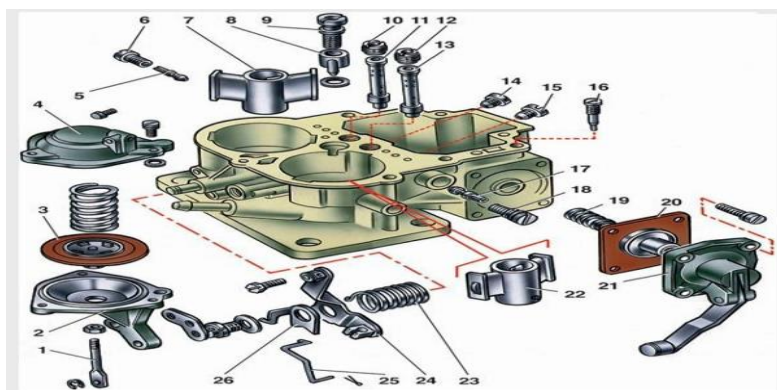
Детали корпуса карбюратора 2107-1107010: 1 – шток пневмопривода второй дроссельной заслонки; 2 – корпус пневмопривода; 3 – диафрагма; 4 – крышка пневмопривода; 5 – топливный жиклер переходной системы второй камеры; 6 – корпус топливного жиклера; 7 – малый диффузор второй камеры; 8 – распылитель ускорительного насоса; 9 – винт-клапан ускорительного насоса; 10 – главный воздушный жиклер второй камеры; 11 – эмульсионная трубка второй камеры; 12 – главный воздушный жиклер первой камеры; 13 – эмульсионная трубка первой камеры; 14 – главный топливный жиклер второй камеры; 15 – главный топливный жиклер первой камеры; 16 – регулировочный винт ускорительного насоса; 17 – топливный жиклер системы холостого хода; 18 – корпус топливного жиклера; 19 – возвратная пружина ускорительного насоса; 20 – диафрагма ускорительного насоса; 21 – крышка ускорительного насоса; 22 – малый диффузор первой камеры; 23 – возвратная пружина рычага; 24 – трехплечий рычаг управления воздушной заслонки; 25 – тяга связи с дроссельной заслонкой; 26 – кронштейн возвратной пружины дроссельных заслонок;
